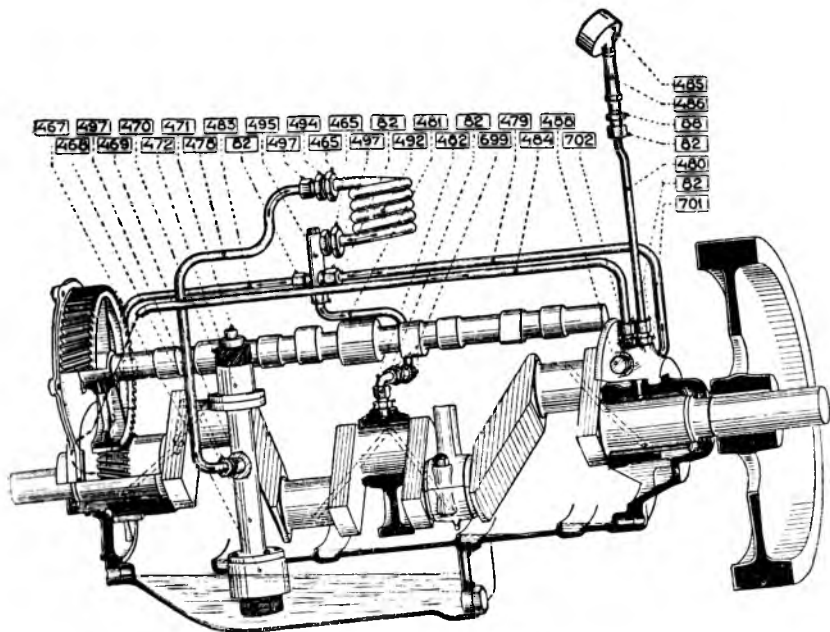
Смазка подшипников коленчатого вала (коренных) и головок шатунов *под давлением*. 467-зубчатый насос внизу вертикальной трубки 468 — 469 и 497, фланец и зажимная гайка отводной нагнетающей трубки 478 — 472 и 470, червячная зубчатка и зажимная гайка на верхнем конце валика 471 насоса. — 483, 479 и 701, отводные нагнетающие трубки к боковым коренным подшипникам, их зажимные гайки 82. — 497, 494 и 465, зажимные гайки и фланцы охлаждающей спирали 492. — 495 фильтр и распределитель по трем трубкам. — 481, 482 и 699, трубка и ее прикрепление к среднему коренному подшипнику. — 484, трубка низкого давления, подающая масло на распределительные зубчатки и ее закрепление 702. — 488, гнездо для дополнительной трубочки. — 485, 486, 88, 480 и 701, манометр и его соединение с нагнетающей трубкой.
